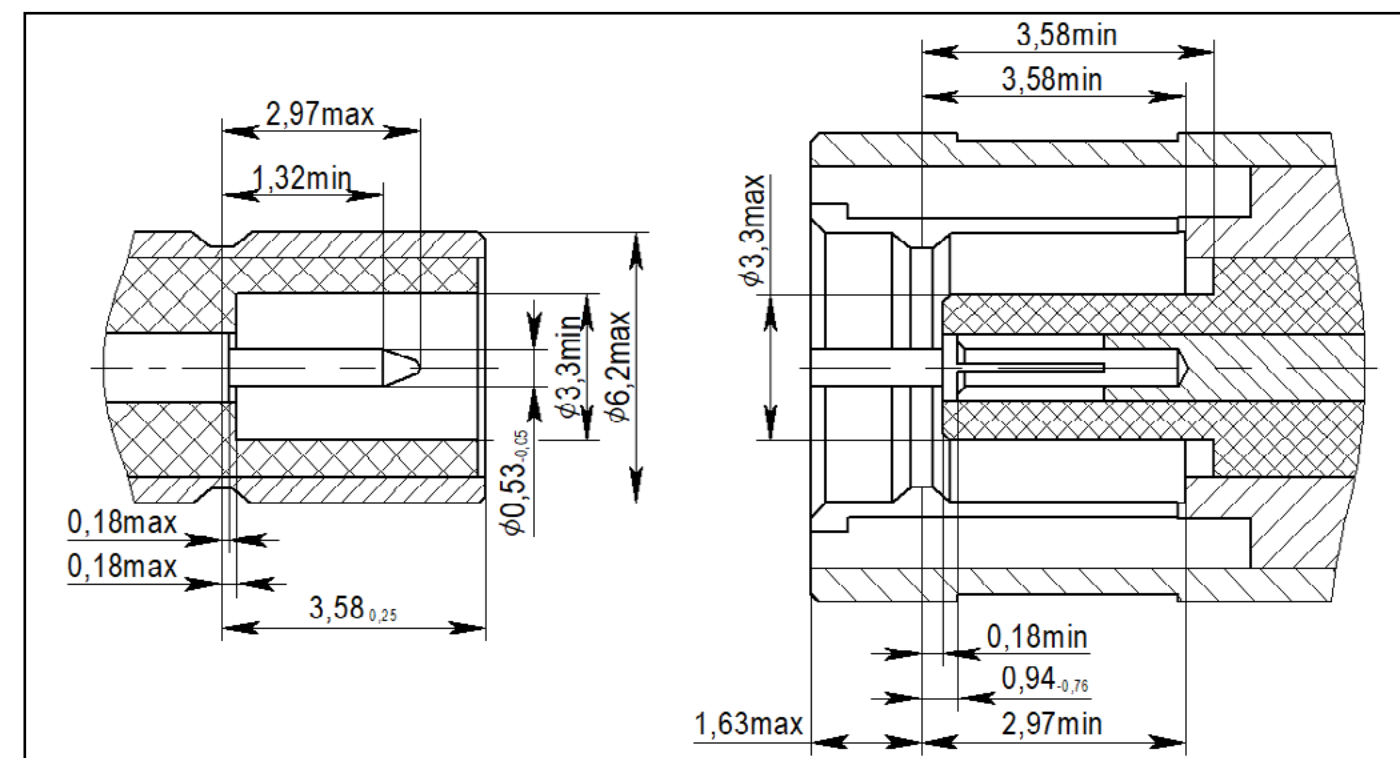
Интерфейс соединителя тип SMB 75 Ом: вилка, розетка (справа)
